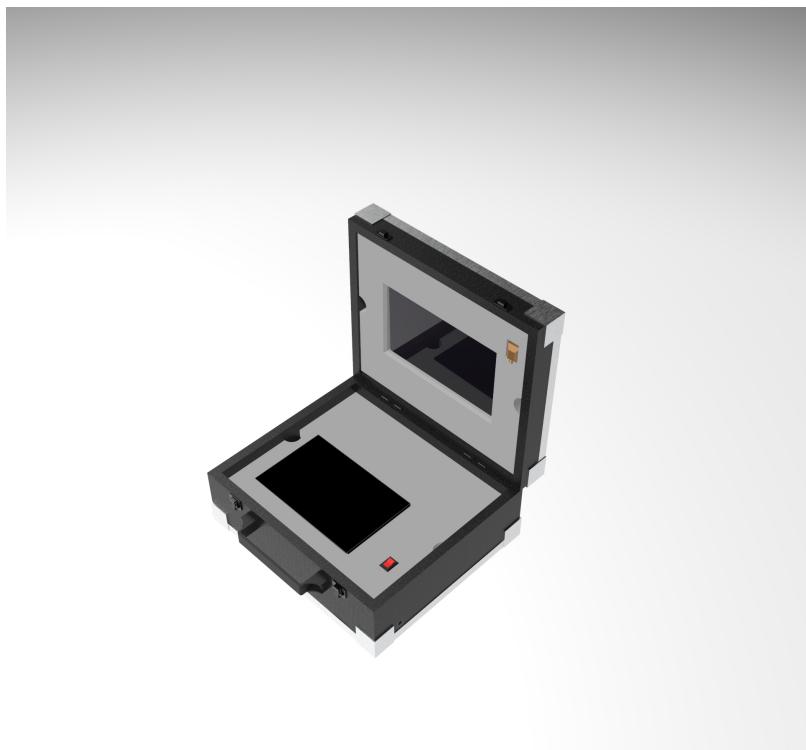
Montagem final da maleta de controle com revestimento e moldura aberta
